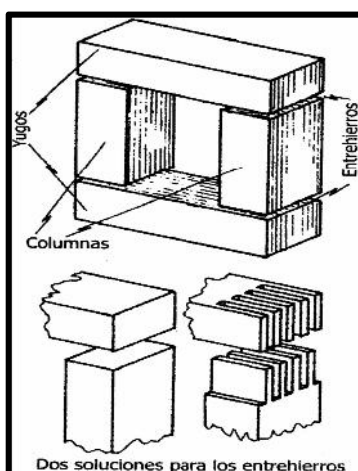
Armado de núcleo con entrehierros planos y dientes de sierra.
